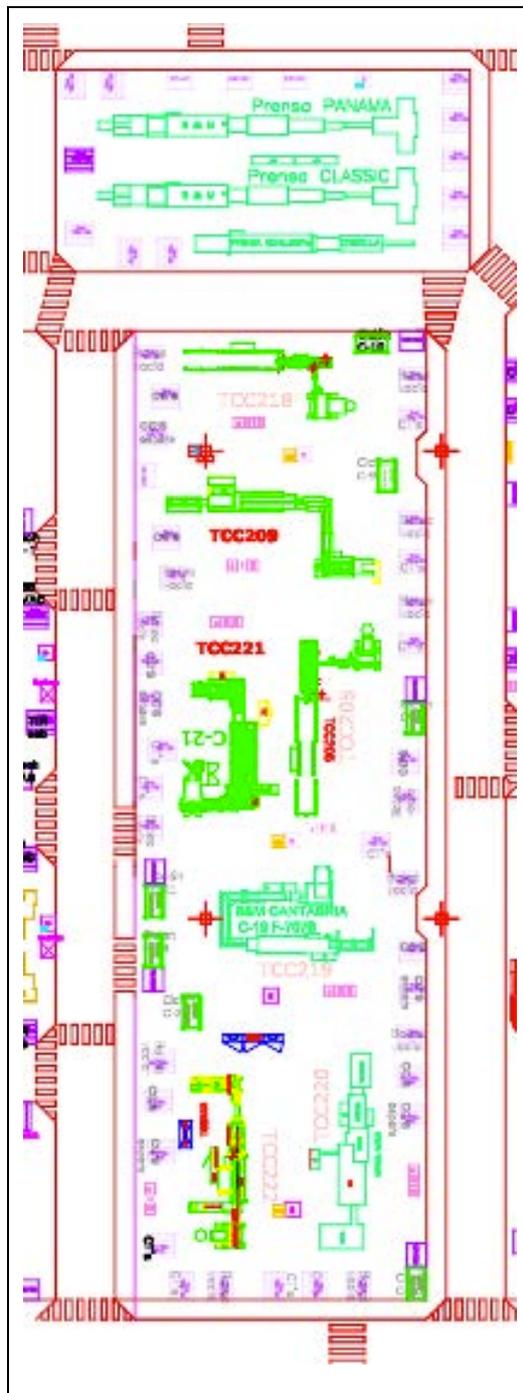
Plano detalle de la zona de cortadoras. [Fuente: Elaboración propia]
